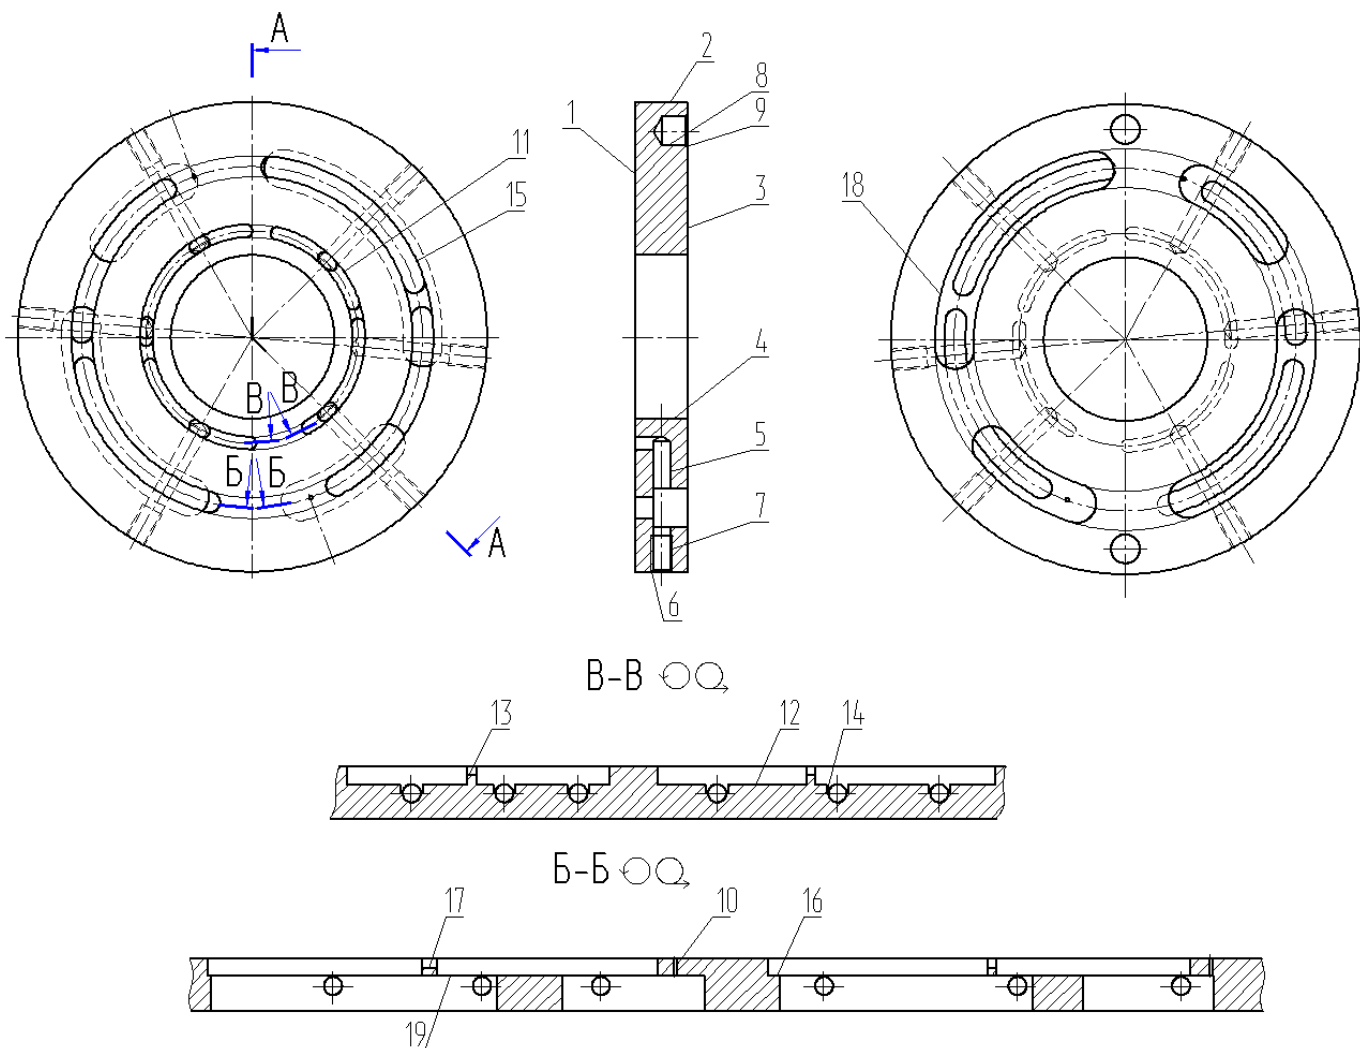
Нумерация поверхностей детали «Диск распределительный»
